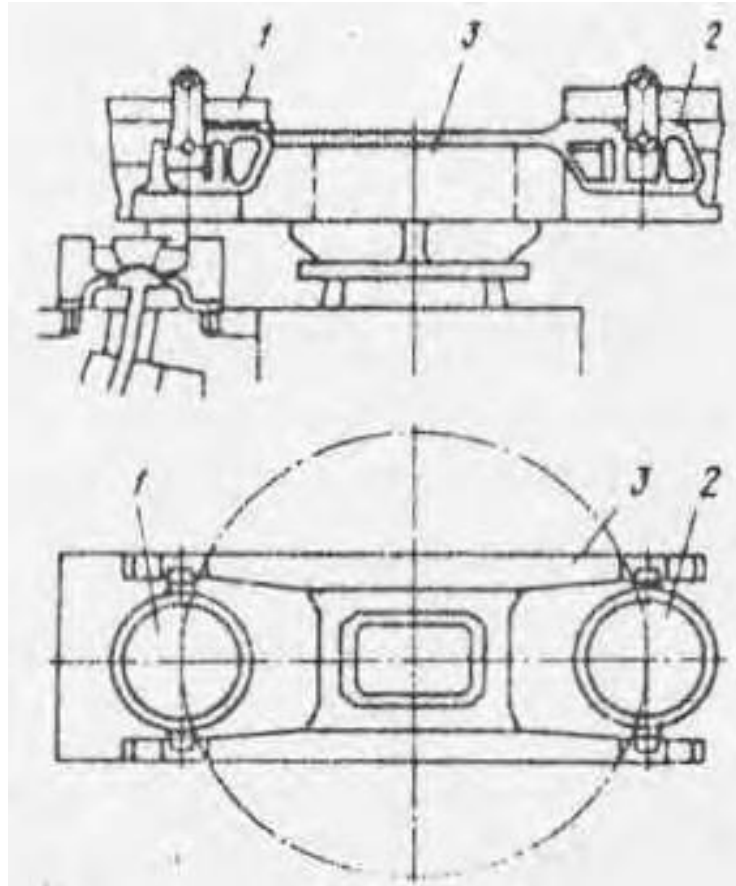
Поворотний стэнд: 1 – сталерозливний, який знаходиться у робочому положенні; 2 – сталерозливний ківш, який знаходиться у резервному положенні; 3 – поворотна консоль стэнда
